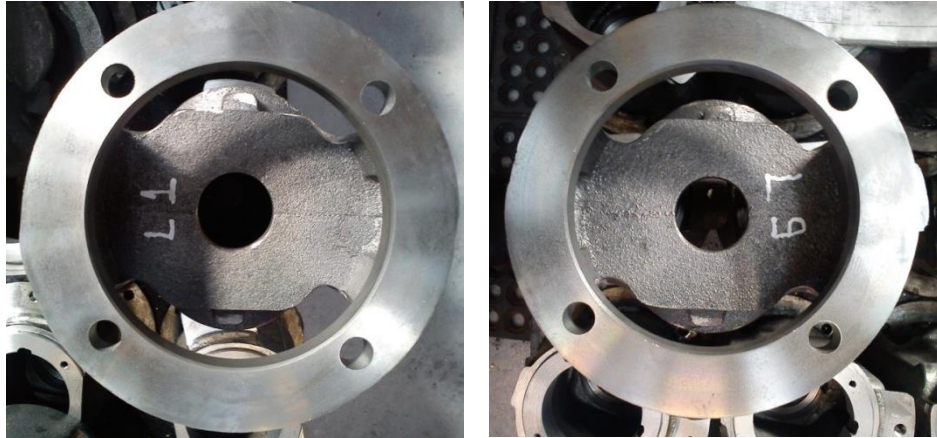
Nuevo sistema de llenado, soporte de rodamiento ZInd 25
